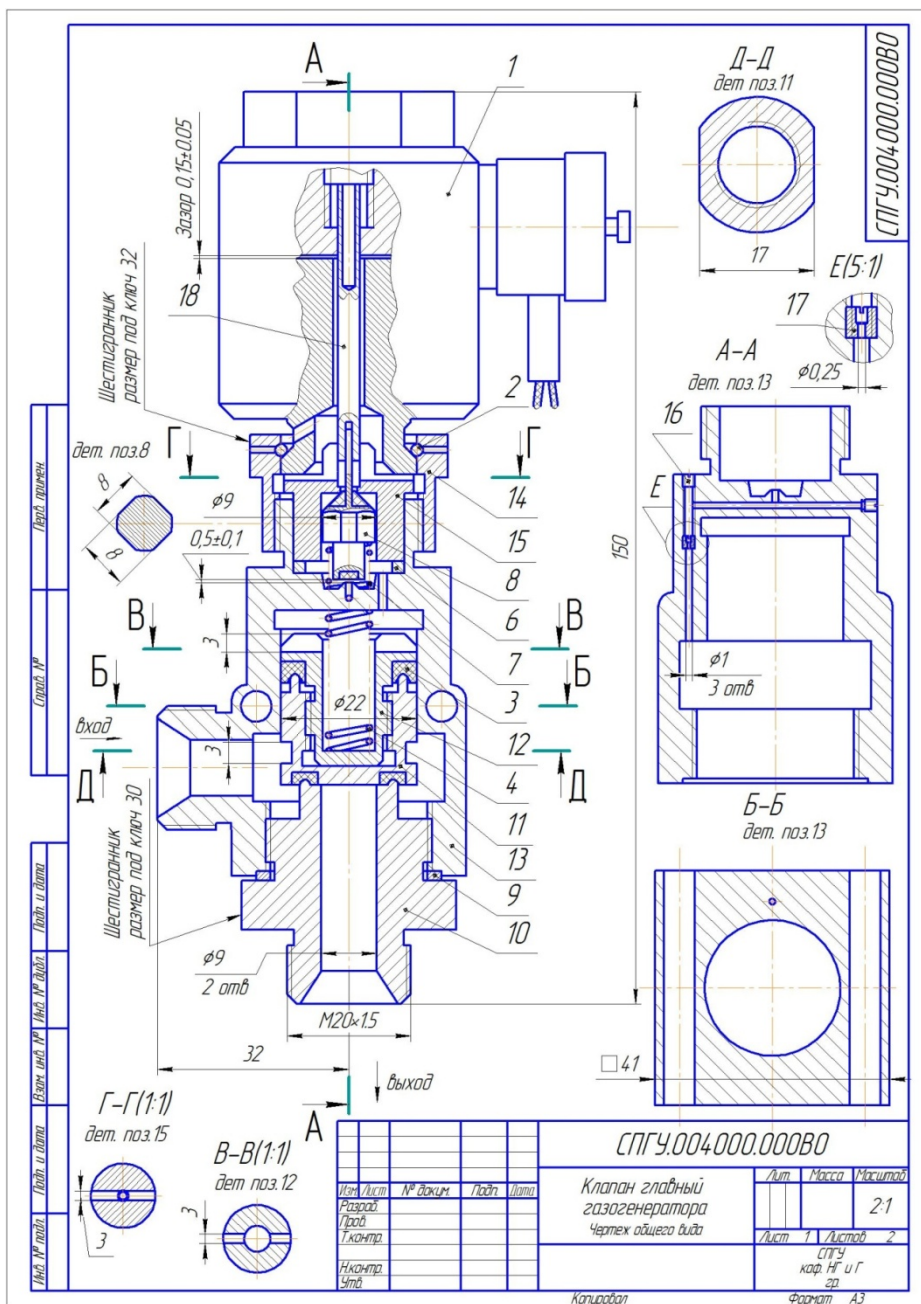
Чертеж общего вида «Клапан главный газогенератора»
